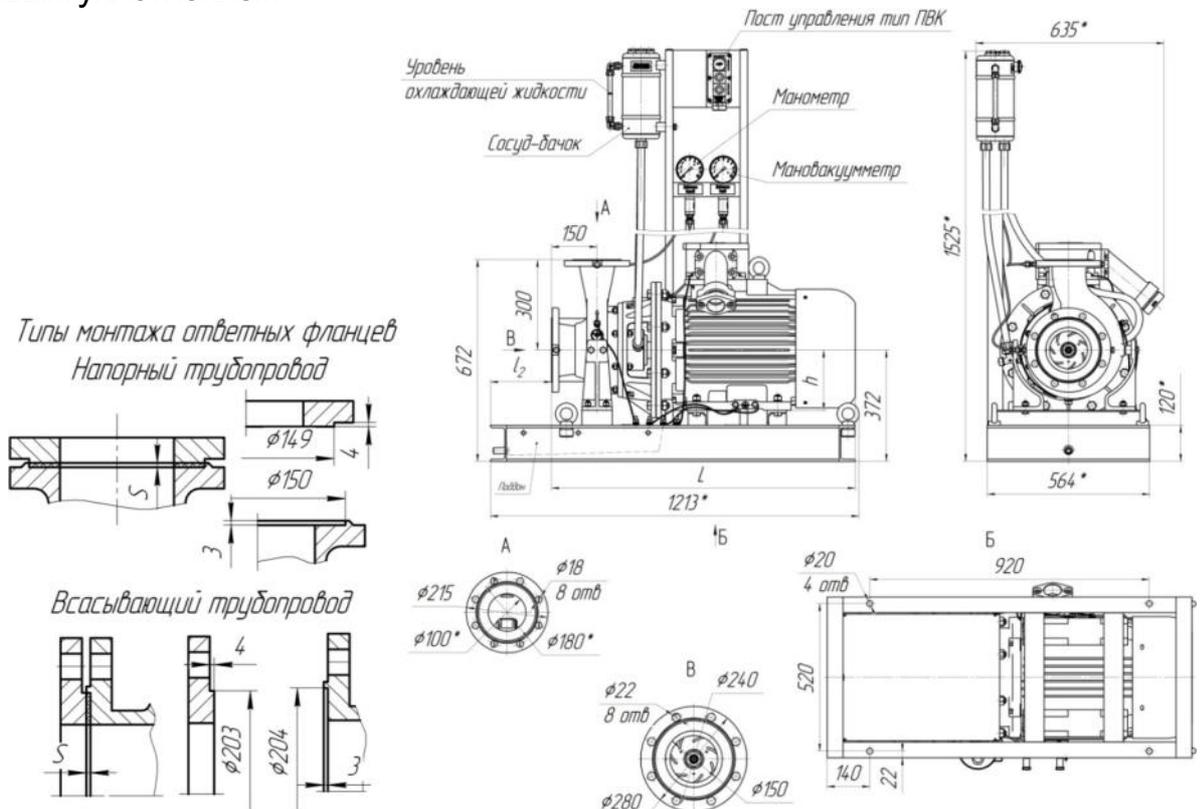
Габаритные и присоединительные размеры КМ 65-50-160E(а,б)-м с двойным торцовым уплотнением
